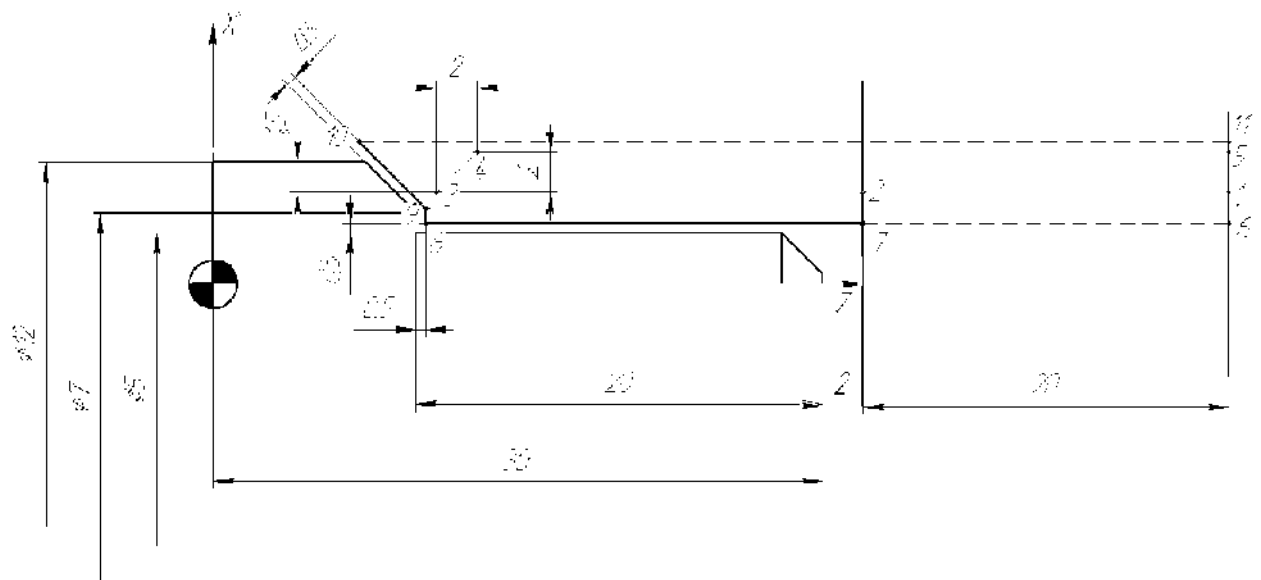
Эскиз обрабатываемой детали и траектория движения инструментов.
